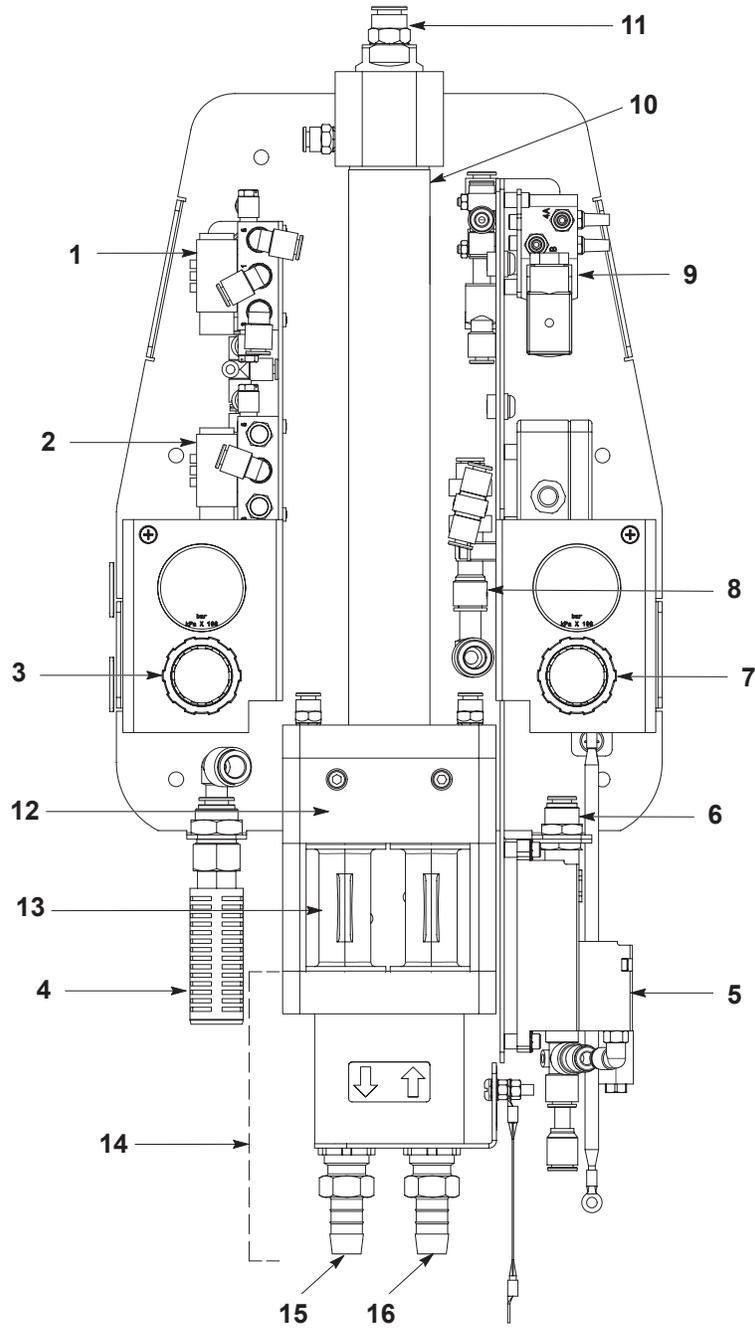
Componentes da bomba (ilustrados com a tampa retirada)
